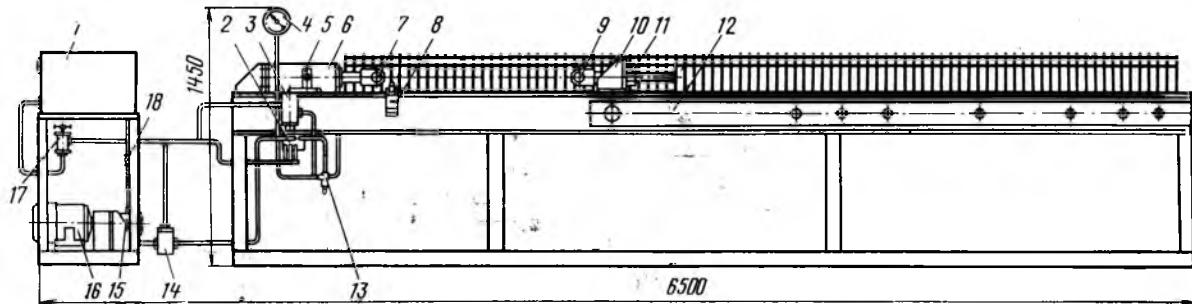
Стенд для испытания грузозахватных приспособлений:
